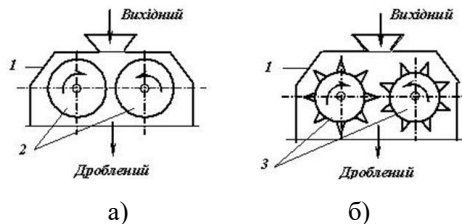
Схема валкової дробарки: а) з гладкими валками; б) з зубчатыми валками; 1 – корпус; 2, 3 – валки
